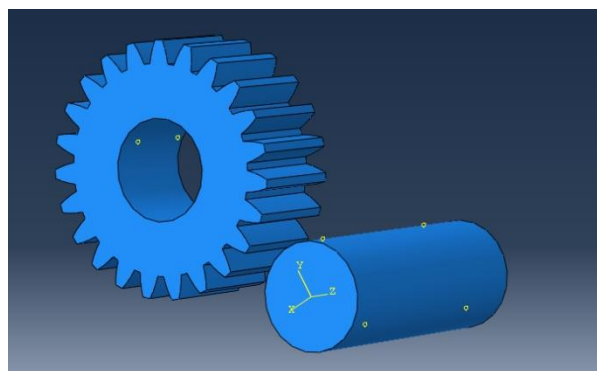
Unión entre un eje y el engranaje pequeño.
